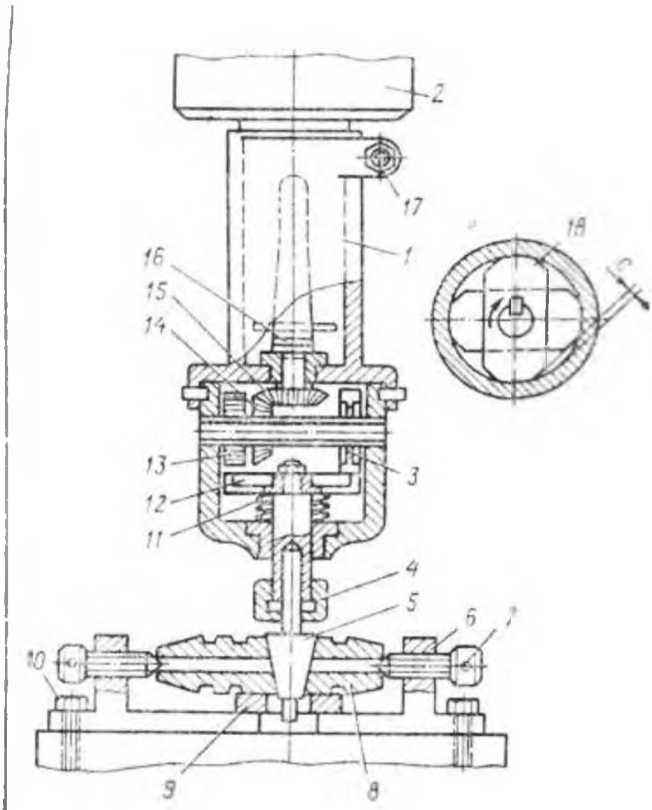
Притирка поверхностей фаски клапана и седла головки блока
